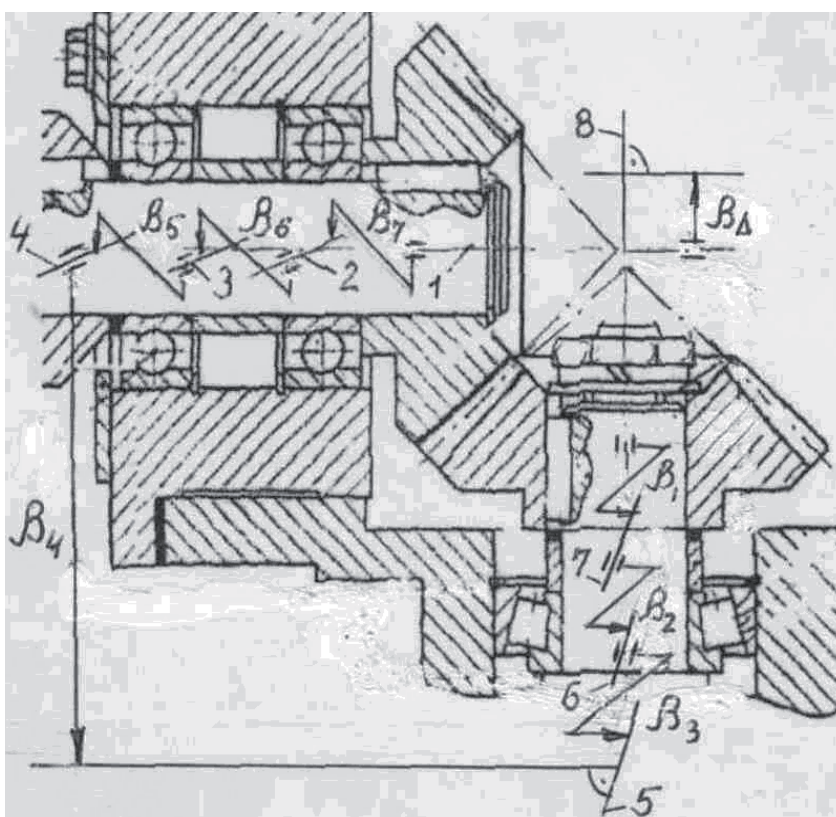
Схема угловой размерной цепи β_{Δ} , определяющей угол скрещивания осей делительных конусов: 1 – ось делительного конуса; 2 – ось базового отверстия колеса; 3 – ось опорной ступени вала; 4 – ось отверстия в корпусе под подшипник; 5 – ось отверстия в корпусе под подшипник второго вала; 6 – ось опорной ступени второго вала; 7 – ось отверстия второго колеса; 8 – ось делительного конуса второго колеса
